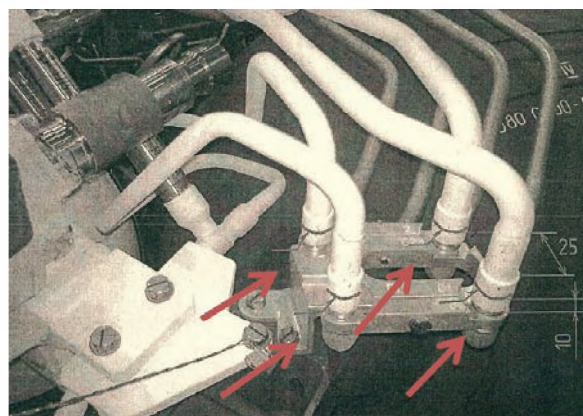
Возможные монтажные условия орбитальной сварки трубопроводов
